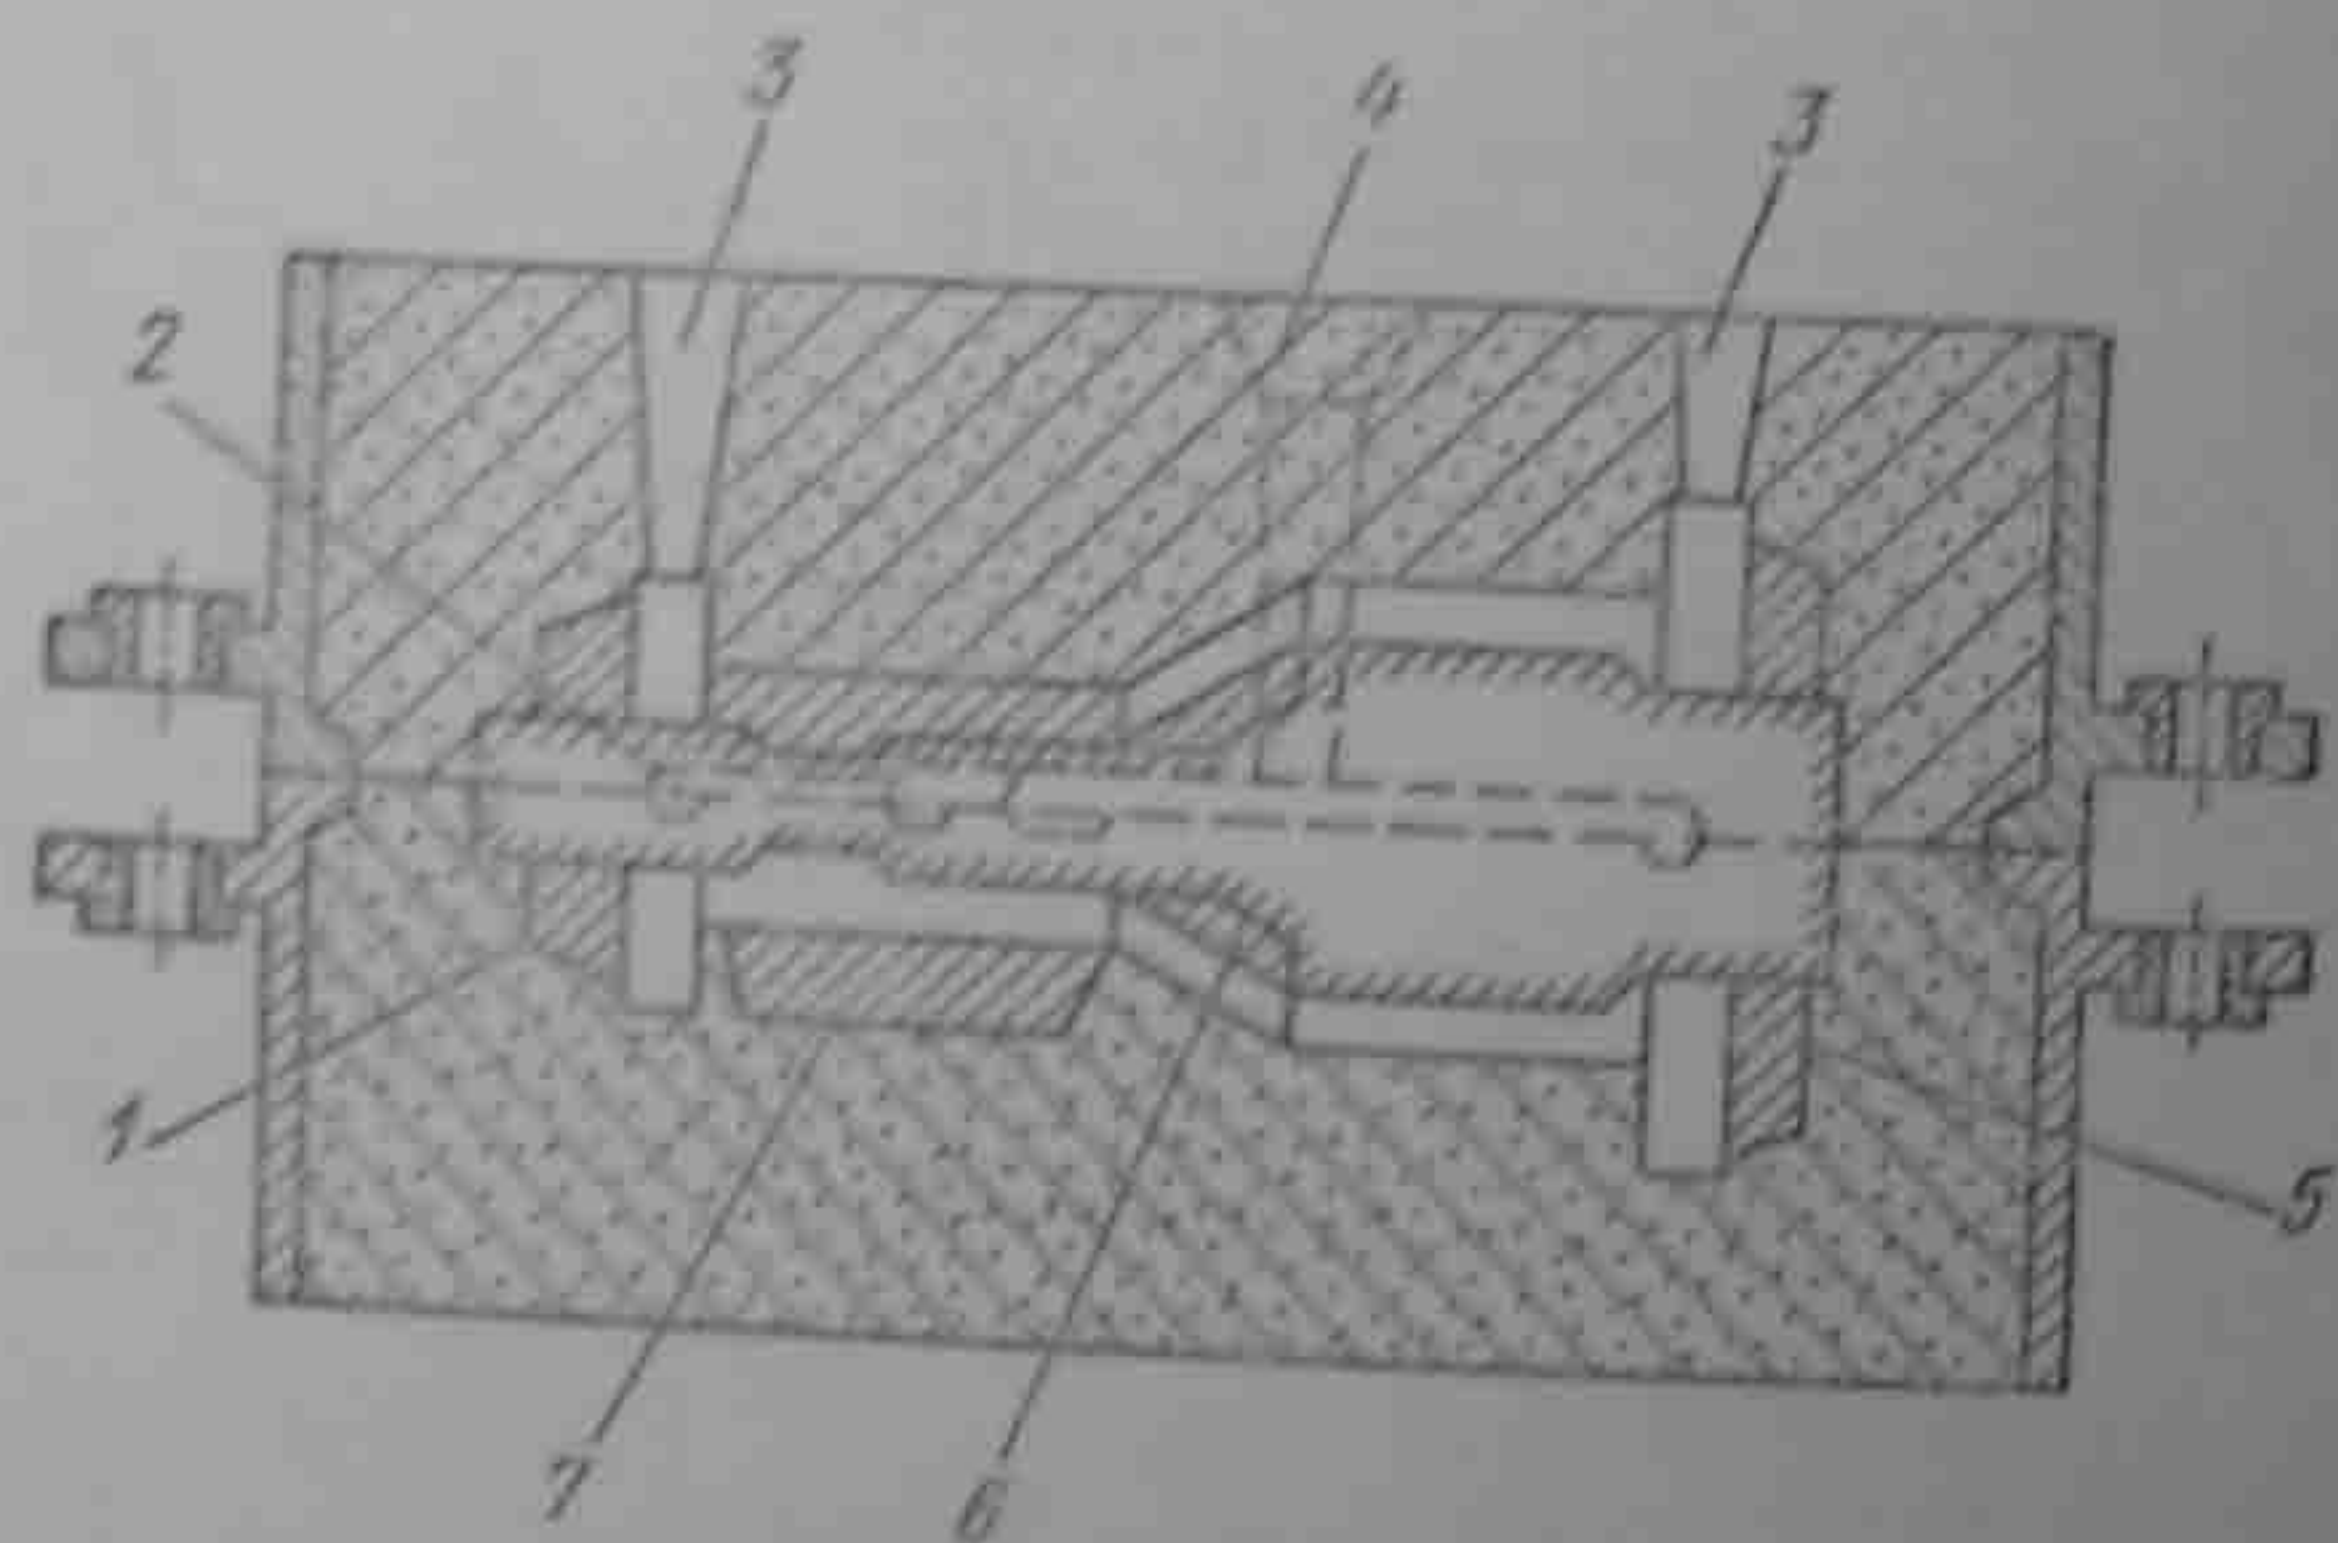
Форма для отливок на алюминиевых сплавах
